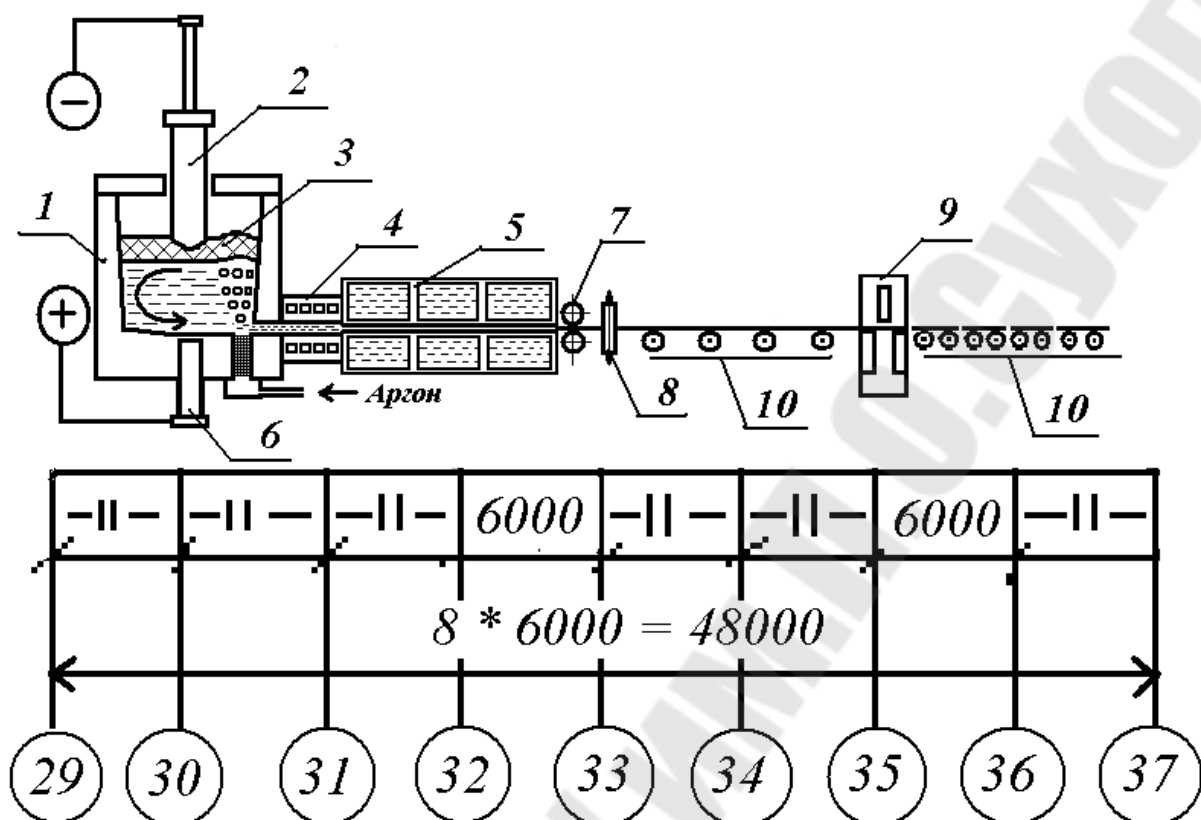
Схема устройства переплава заготовки (электрода) и изготовления тонкой литой отливки (сутунки). (К рис.19).
